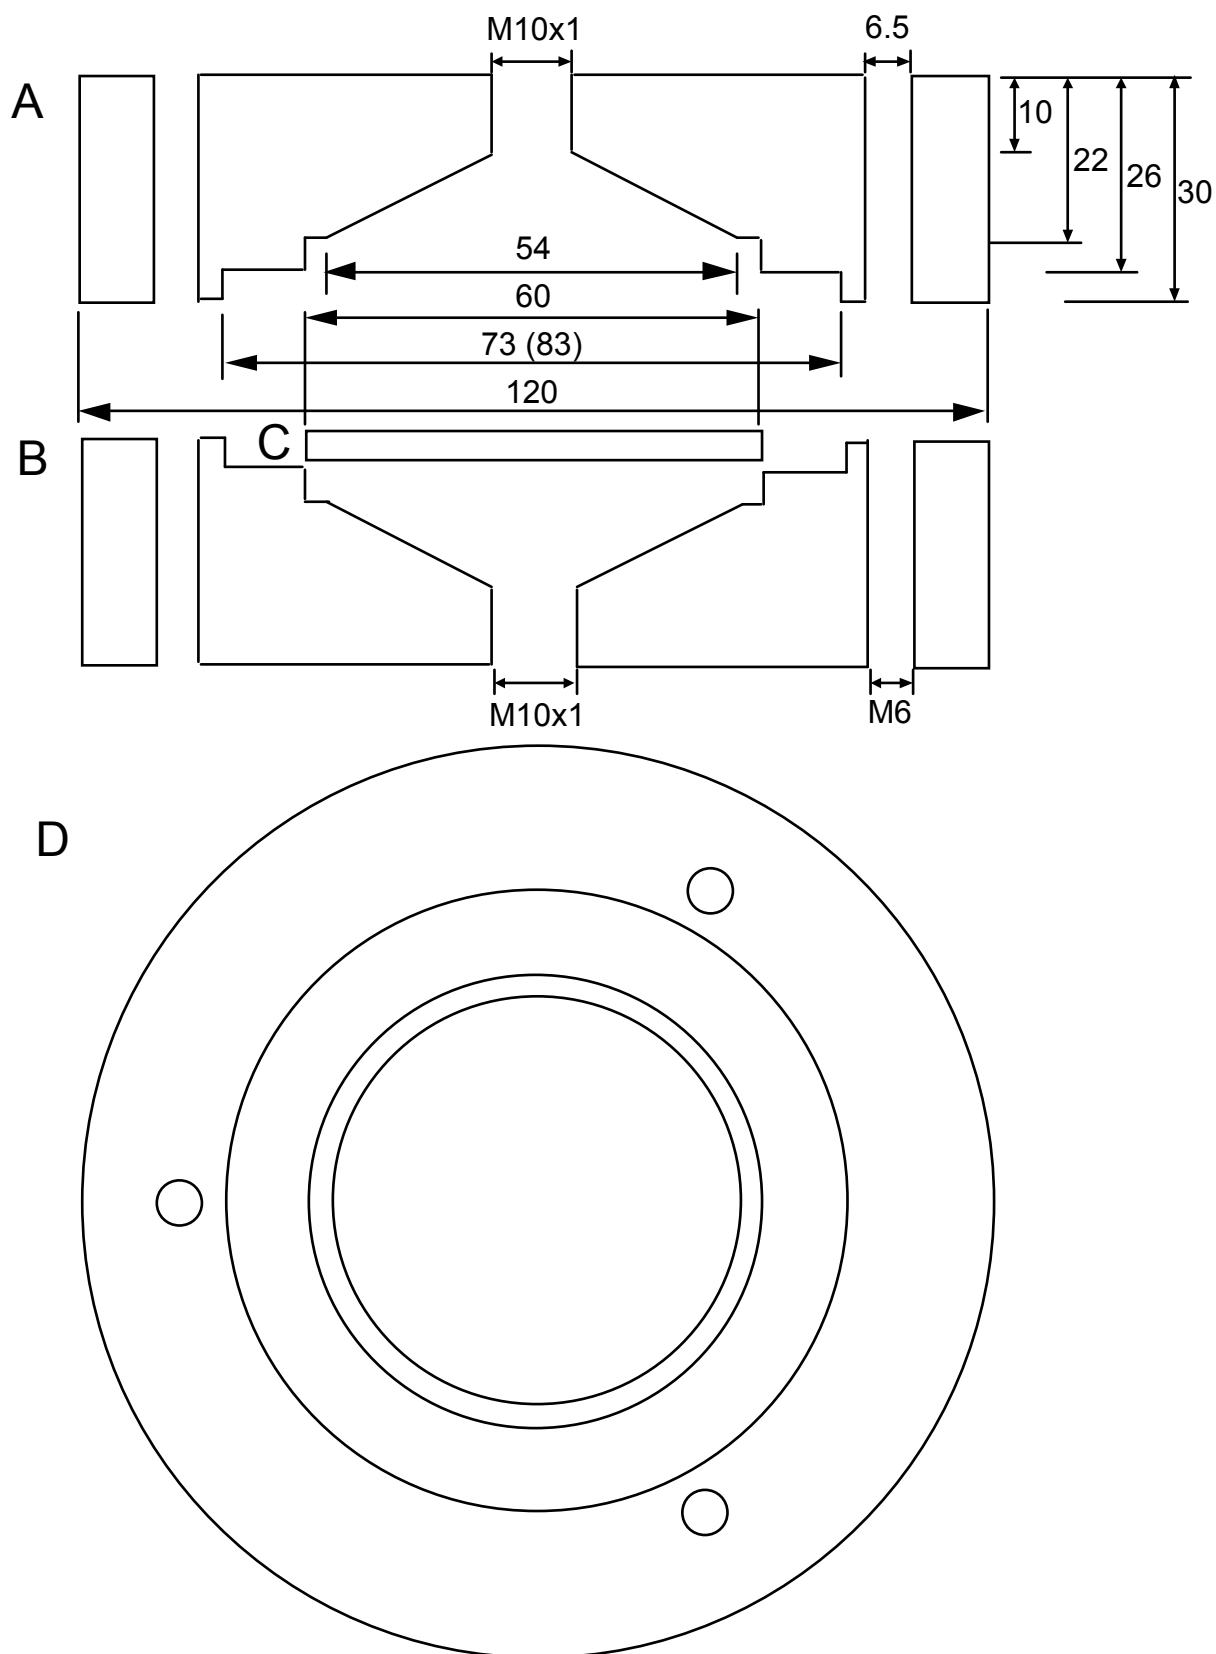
Konstruktionsskizze der Plexiglasteile des Permeameters (Massangaben in mm). A: Aufriss der Deckplatte; B: Aufriss der Bodenplatte; C: Lochplatte mit ca. 200 – 250 Löchern ($\varnothing = 2$ mm); D: Grundriss von Deckplatte und Bodenplatte. Die Massangaben in Klammern stehen für die Version des Permeameters, das die Messung von Proben mit $\varnothing = 57$ mm im Paraffinmantel (ca. 2 mm) erlaubt
